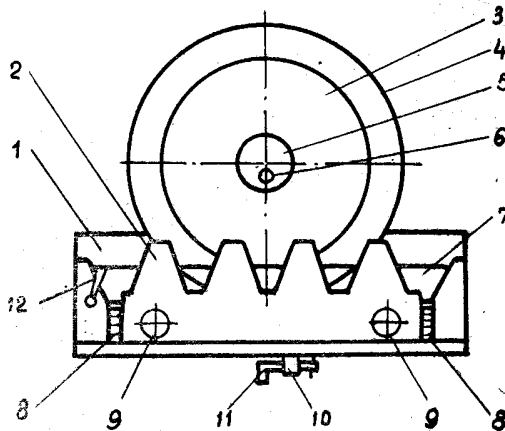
Прибор для вычерчивания зубьев эвольвентного профиля
